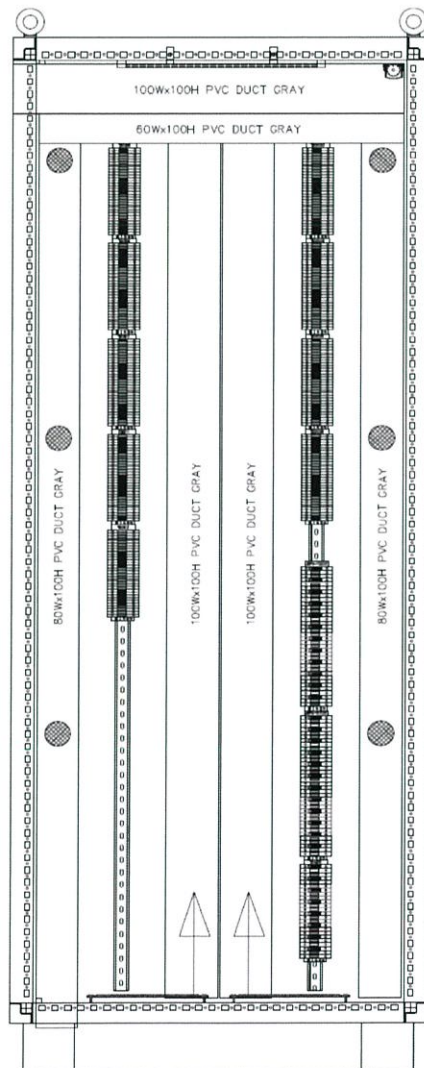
Layout ด้านหน้าตู้ Marshalling 2
